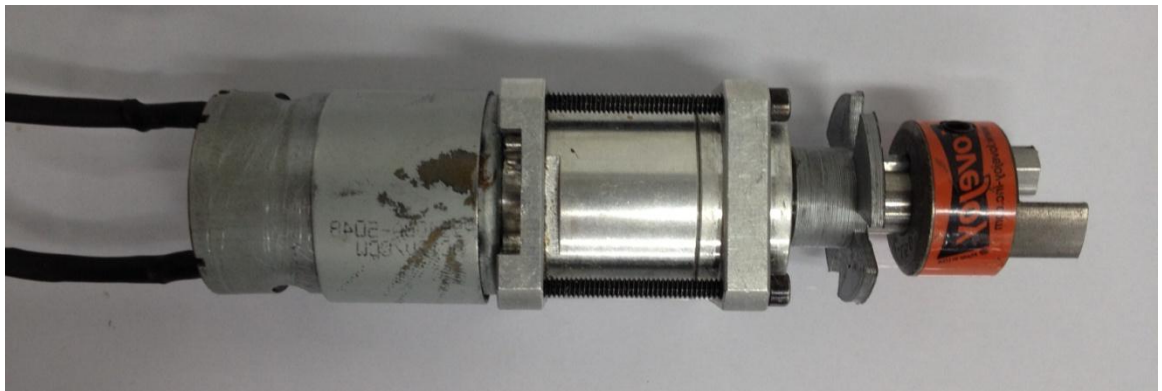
Acople, espaciador, pieza para centrar y rodamiento ensamblados en el tornillo
